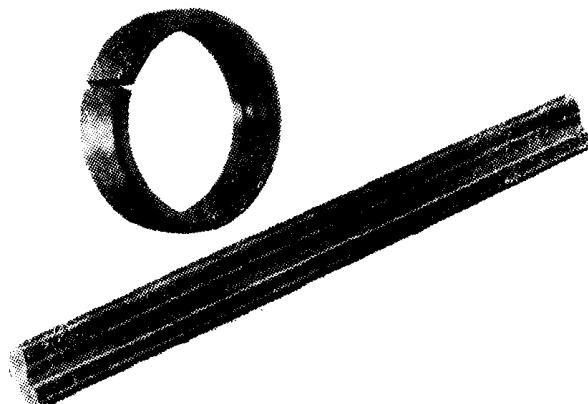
热轧、冷拔、焊接加工生产的206轴承圈示意图
